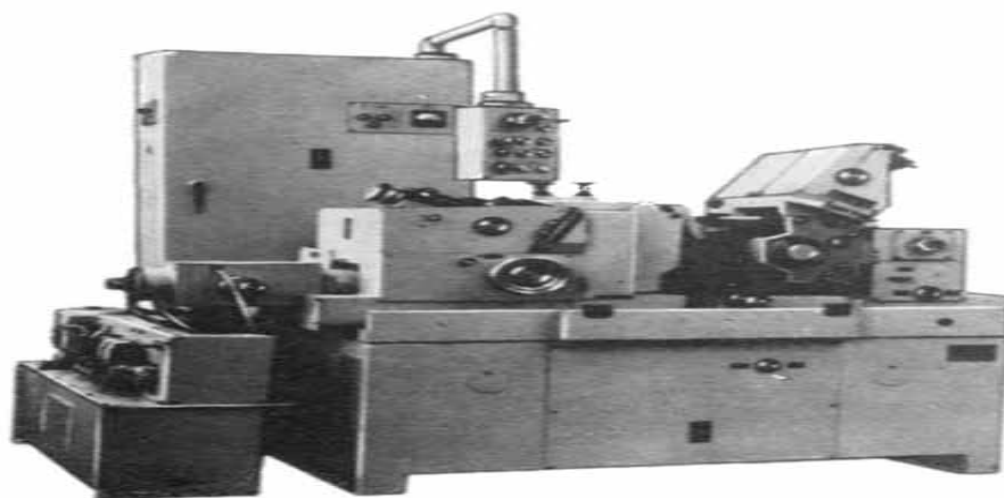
3М182 станок круглошлифовальный бесцентровый (бесцентровошлифовальный)
